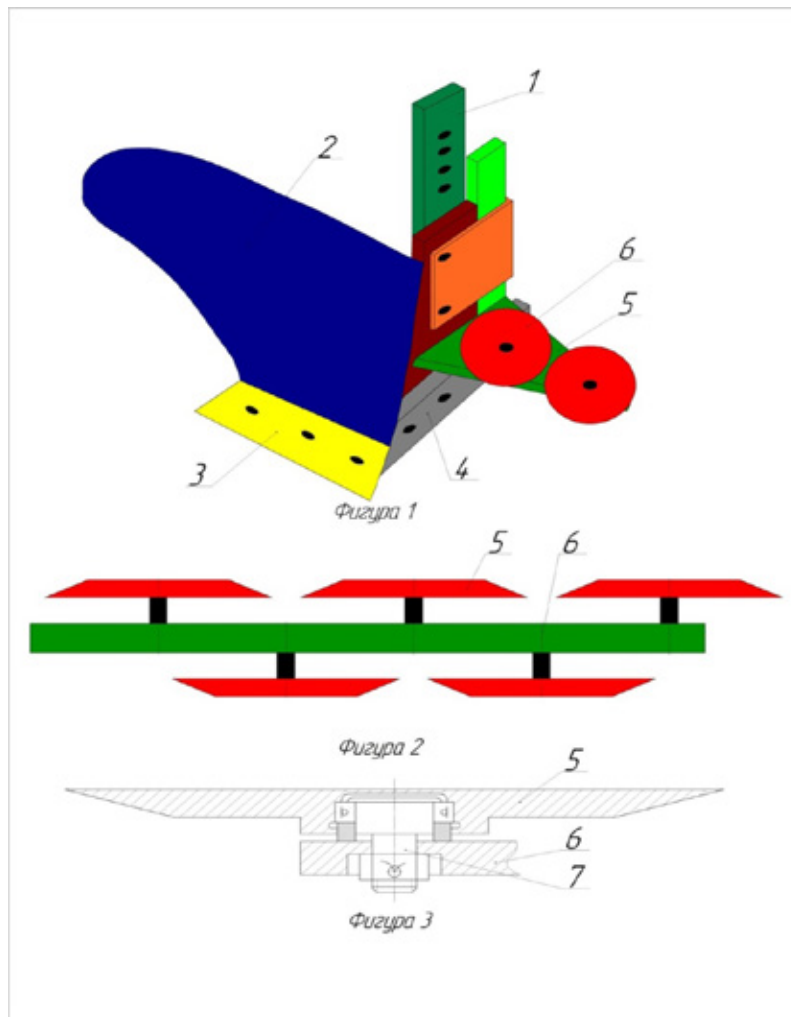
Схема предлагаемой конструкции плоскорежущего рабочего органа лемешного плуга: 1 — стойка корпуса плуга, 2 — отвал, 3 — лемех, 4 — полевая доска, 5 — плоскорежущая бритва, 6 — диск, 7 — ось крепления диска
